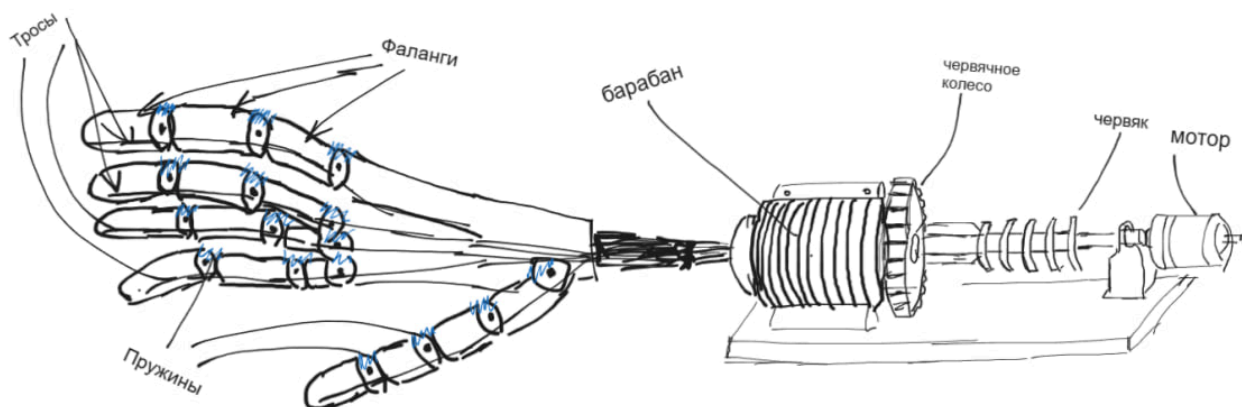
Зарисовка роборуки на основе механизма червячного редуктора
